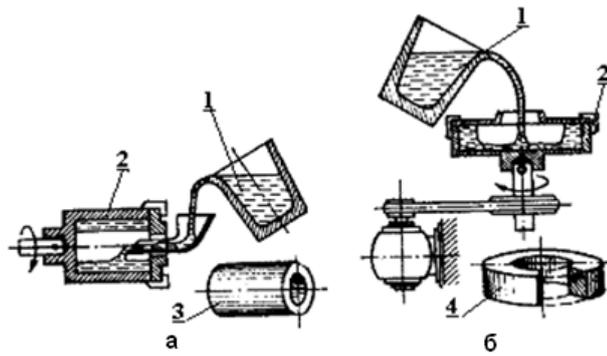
Схемы изготовления отливок на центробежных машинах с осью вращения: а – горизонтальной; б – вертикальной ; 1 – расплав, 2 – вращающаяся форма, 3 – отливка (труба), 4 – отливка (венец)
